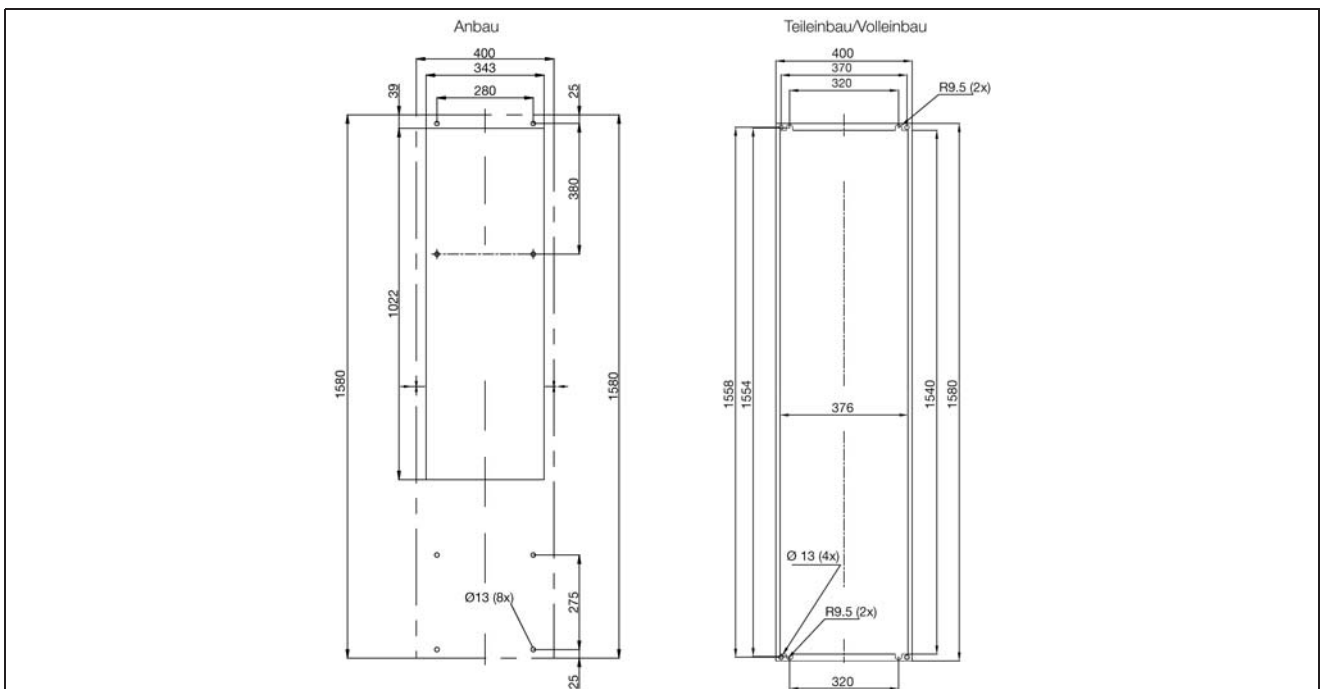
Montageausschnitt für Anbau/Teileinbau/Volleinbau
